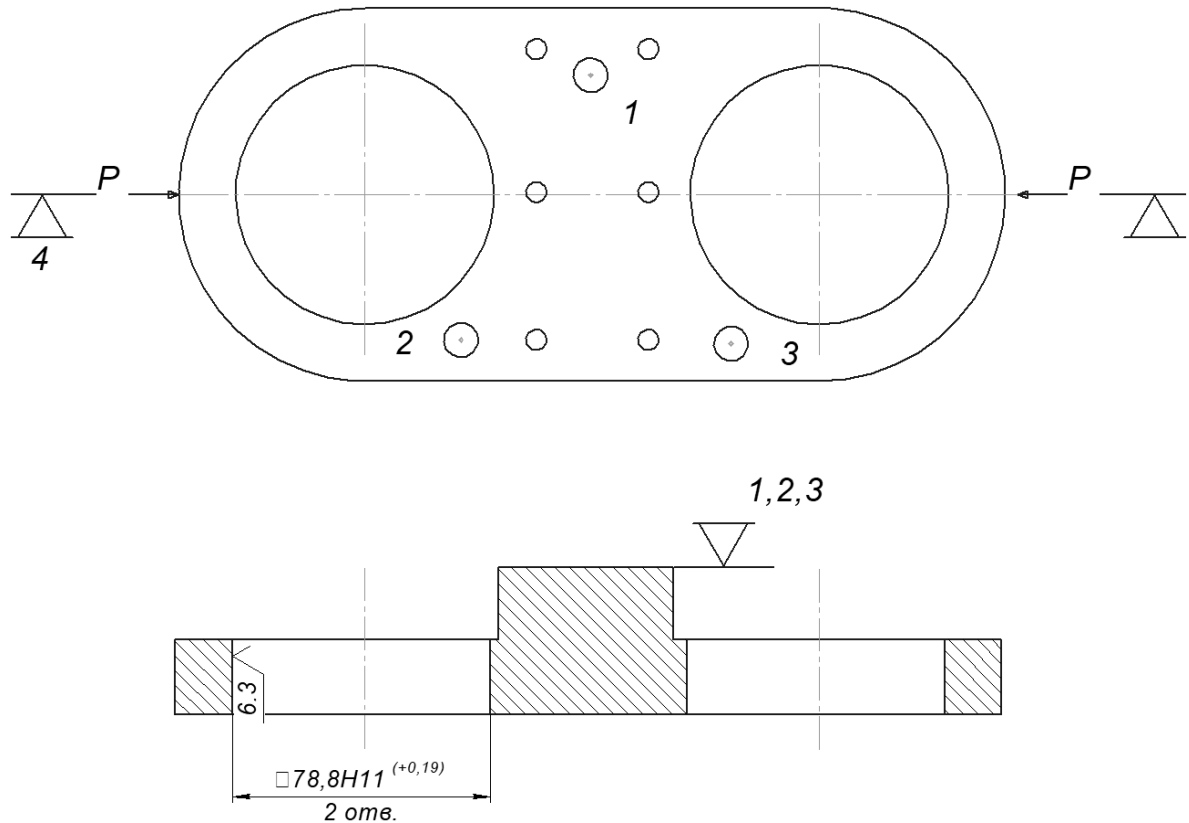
Схема установки деталі при чорновій обробці розміру $\varnothing 80H8$
